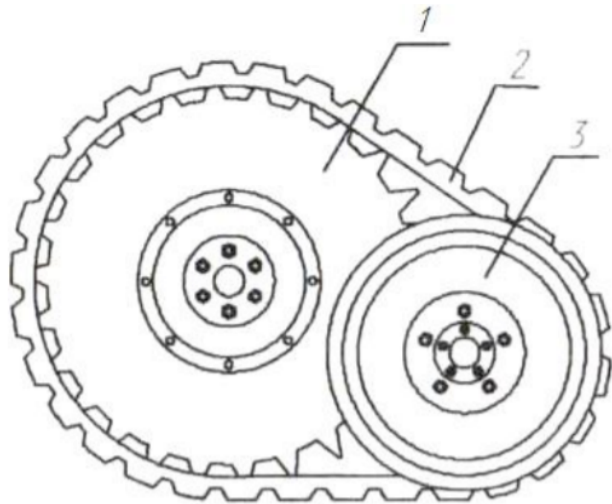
Полугусеничный движитель с направляющими дисками
